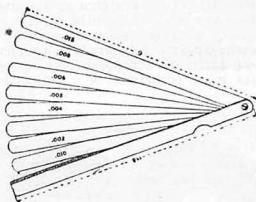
Щупы для проверки зазоров между стенками цилиндров и поршней
